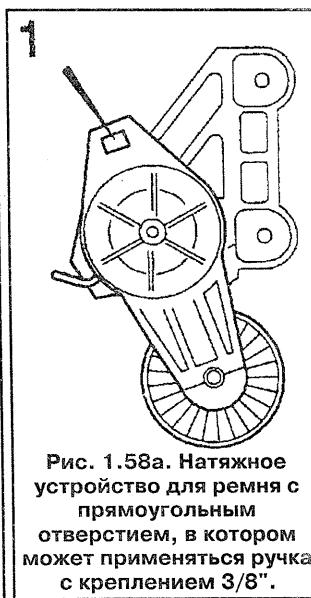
а. Натяжное устройство для ремня с прямоугольным отверстием, в котором может применяться ручка с креплением 3/8".
